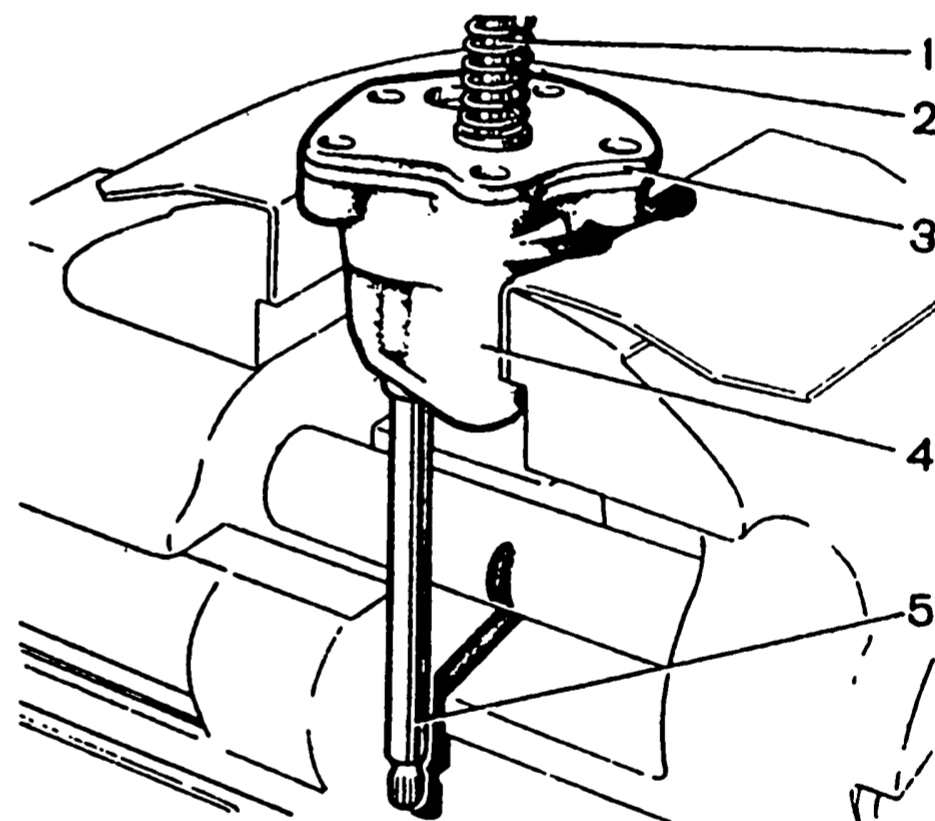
Разборка масляного насоса: 1 - редукционный клапан; 2 - пружина; 3 - крышка; 4 - корпус; 5 - валик
